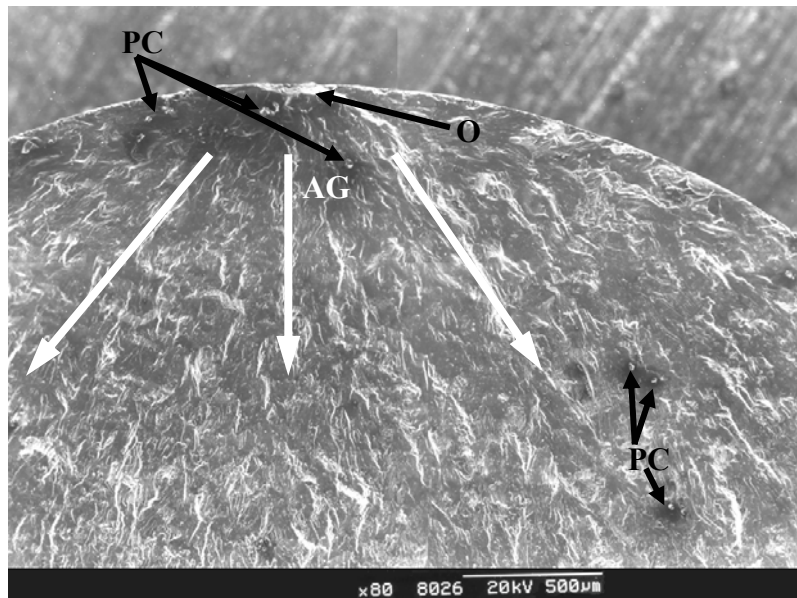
Inicio de grieta en superficie de fractura de la probeta N° 3
